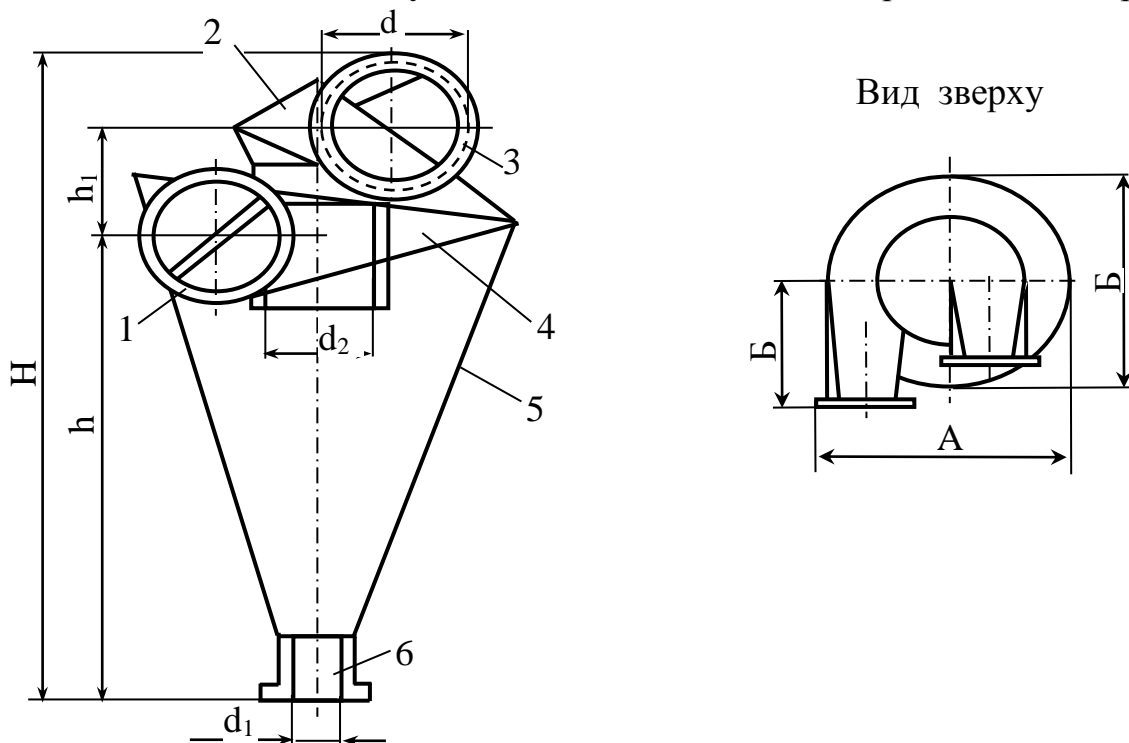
Циклони конструкції СИОТ: 1 – вхідний патрубок забруднених газів; 2 – розкручувач; 3 – патрубок для відведення очищених газів; 4 – кришка; 5 – корпус у вигляді конуса; 6 – патрубок для видалення пилу
